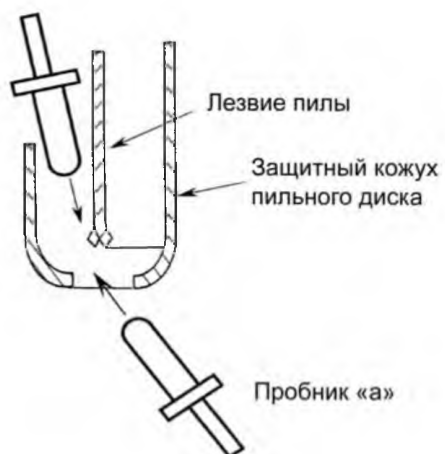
Отверстие для пильного диска и/или расклинивающего ножа в нижнем защитном кожухе и отверстие верхнего защитного кожуха
